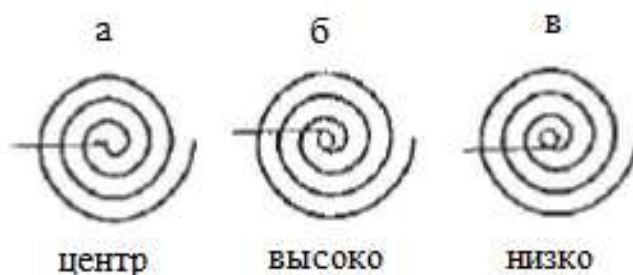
Результат калибровки высоты резца (а: правильная калибровка, б: резец высоко, в: резец низко).
